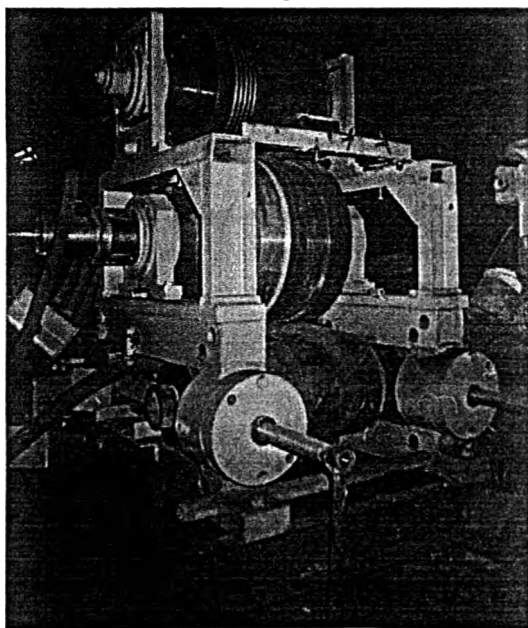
Экспериментальная установка непрерывного литья в кристаллизатор типа колесо – лента
